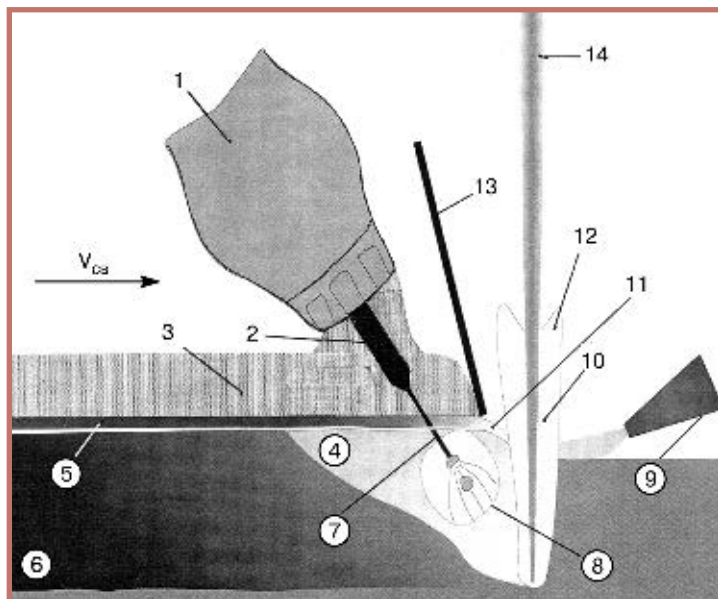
Схема гибридной лазерно-дуговой сварки под флюсом (LUPuS): 1 — бункер для флюса; 2 — контактный мундштук; 3 — флюс; 4 — ванна жидкого металла; 5 — шлаковая корка; 6 — металл сварного шва; 7 — сварочная проволока; 8 — зона горения дуги; 9 — сопло подачи гелия; 10 — парогазовый канал; 11 — расплавленный флюс; 12 — исходящие плазма и пары металла; 13 — разделительная пластина; 14 — лазерный пучок
